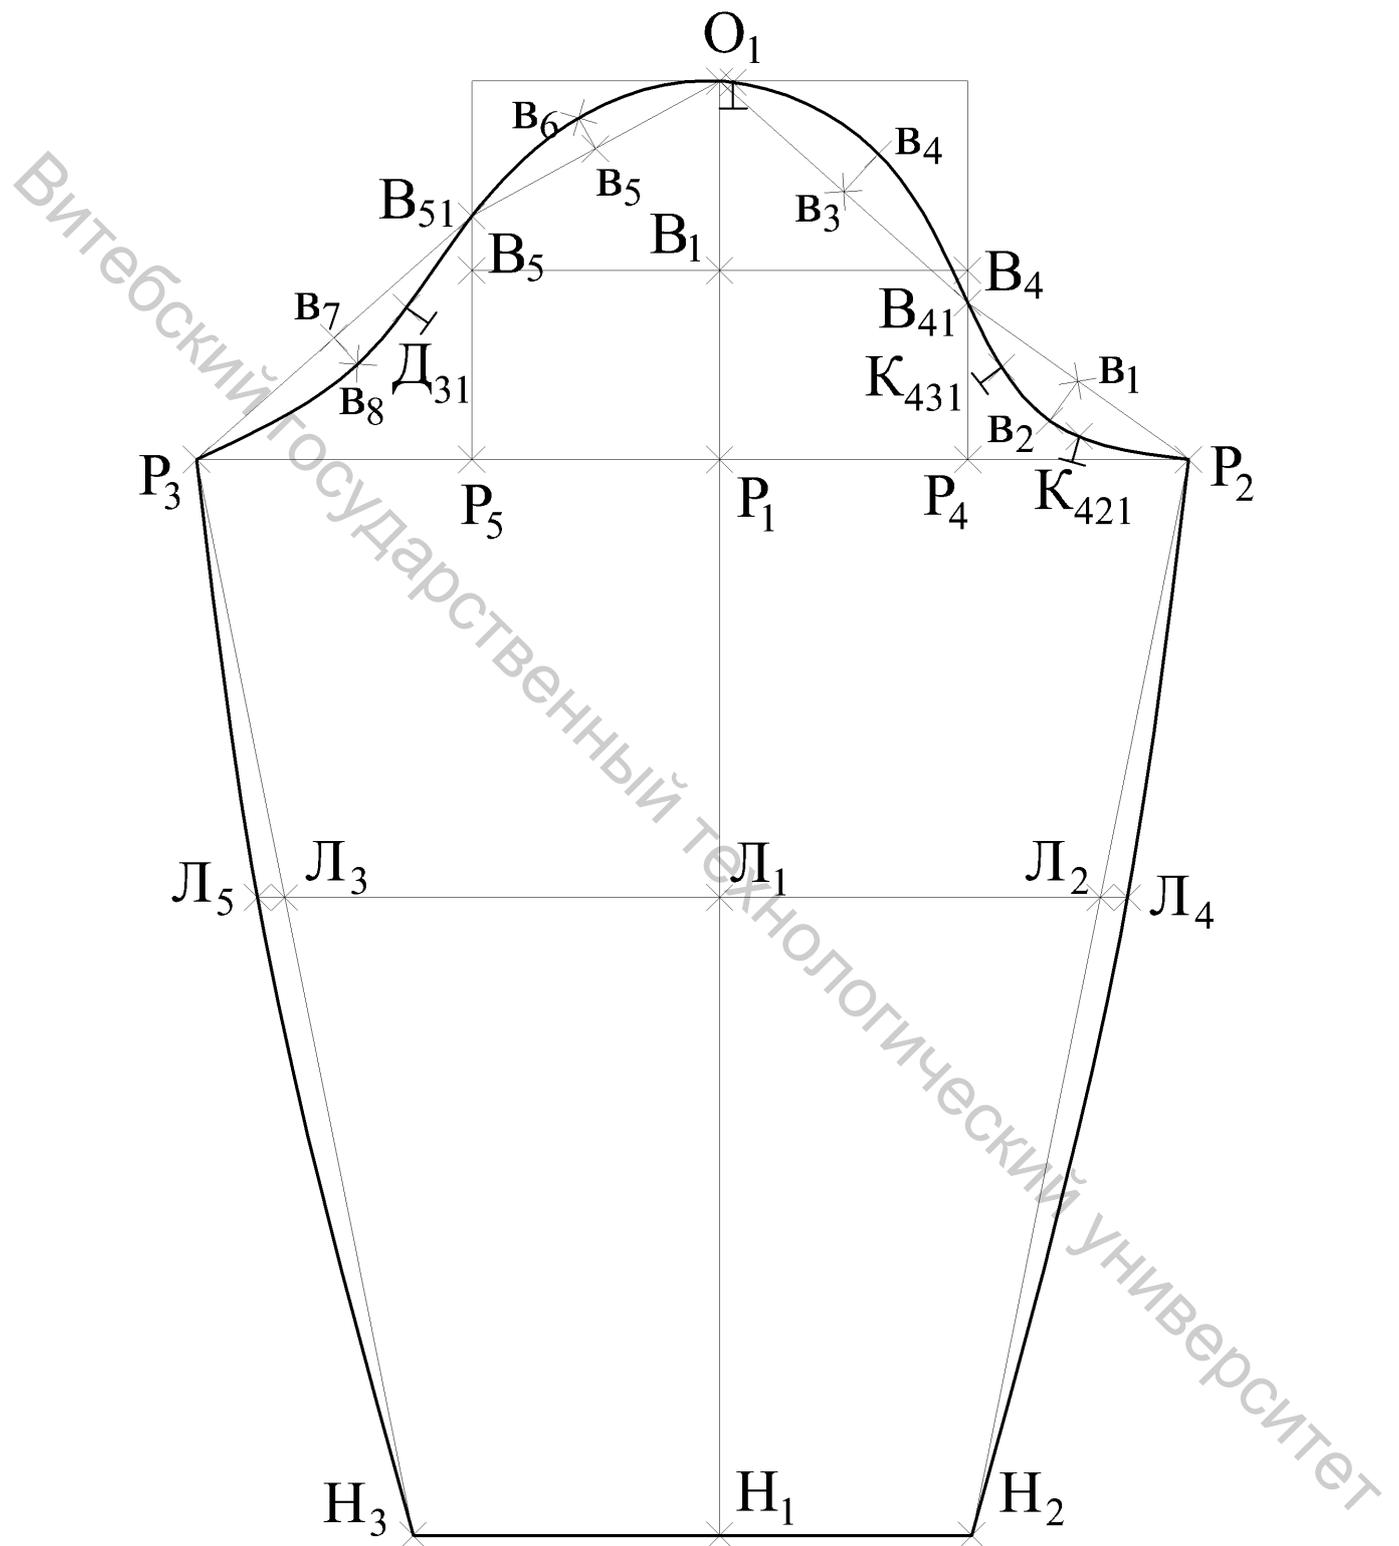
Чертеж конструкции рукава джемпера полурегулярного
